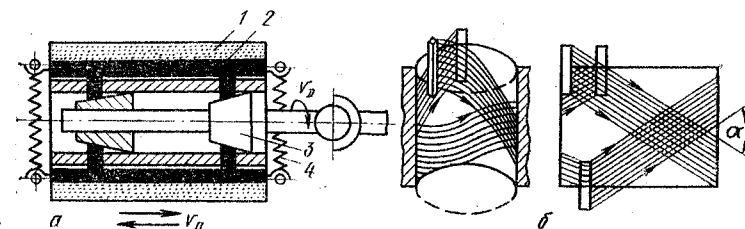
Схема обработки цилиндрического отверстия хонингованием
